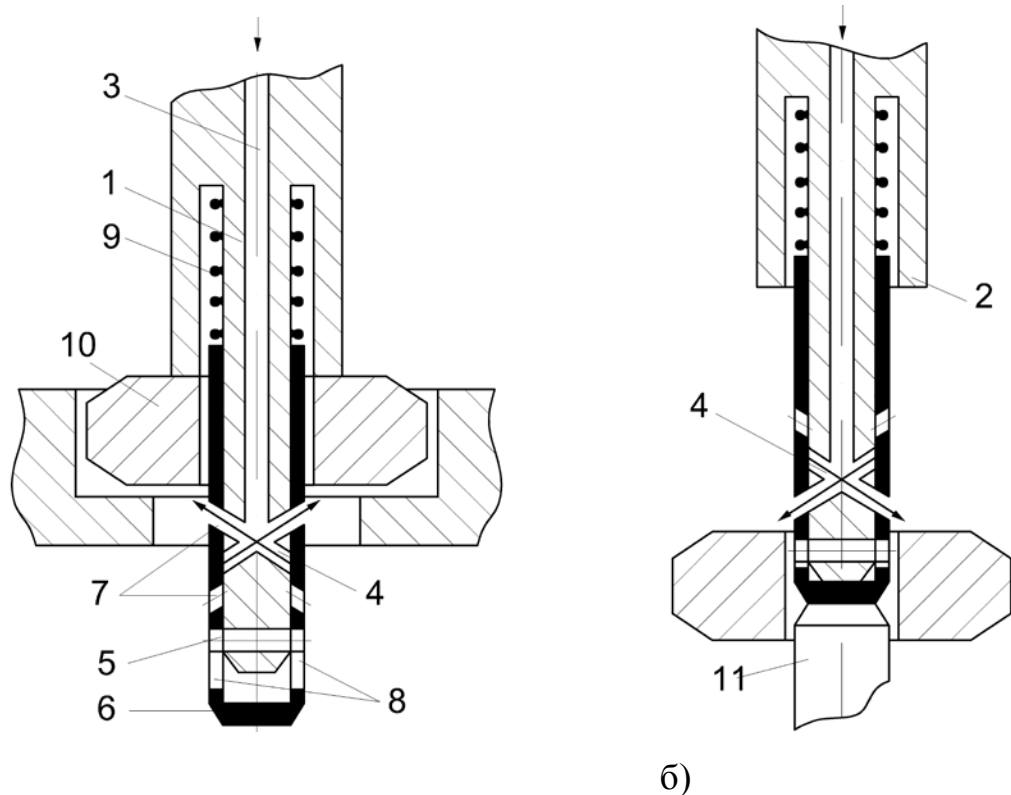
Струминний захоплювач: а) – положення захоплення деталі;
